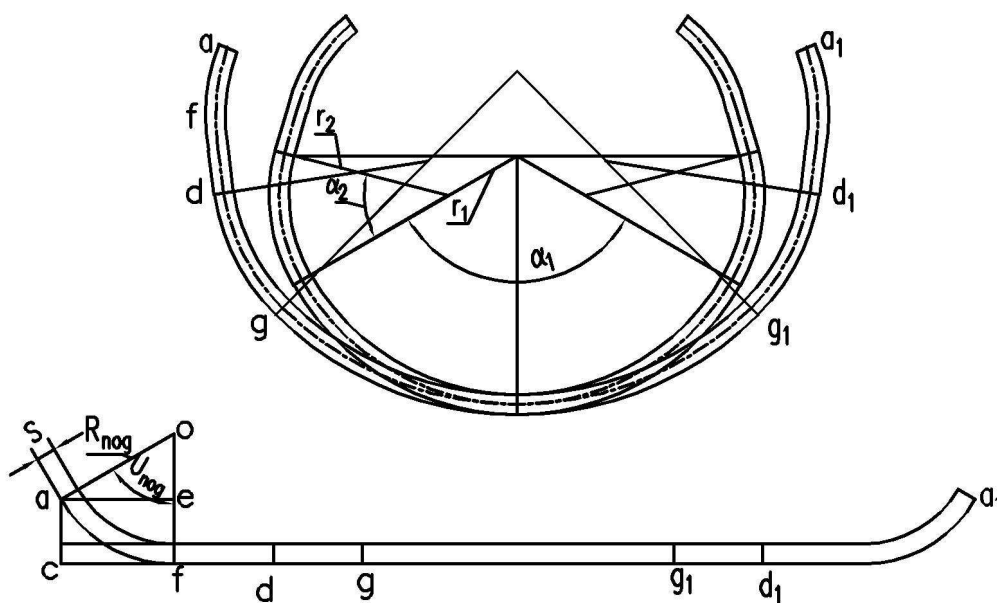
Схема формовки заготовки двухрадиусным пуансоном
